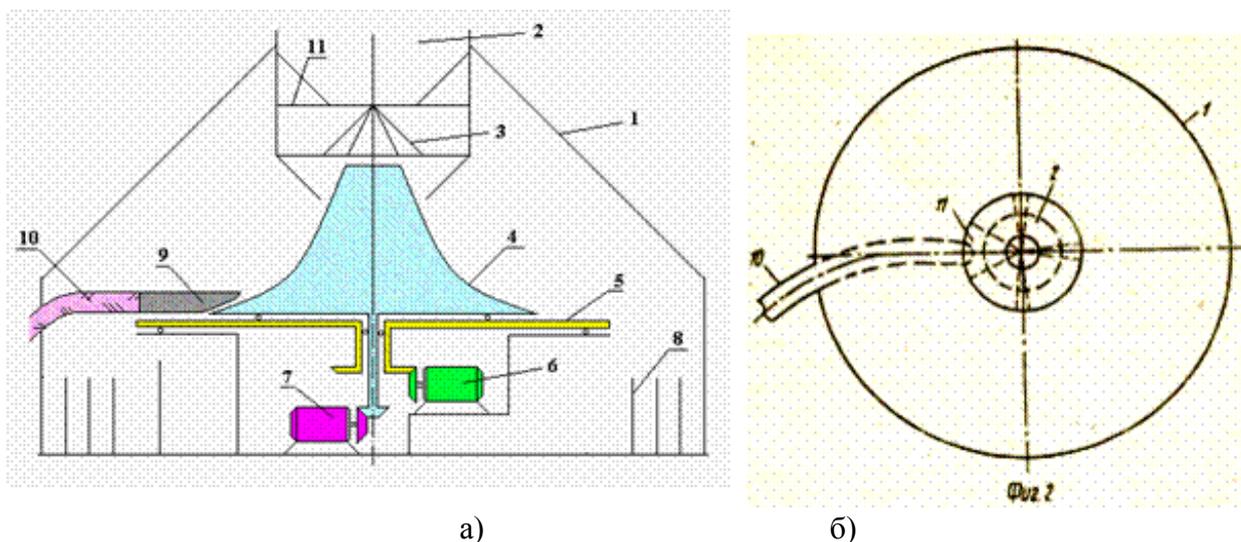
Фрикционный сепаратор: осевой разрез (а) и вид сверху (б): 1 – корпус, 2 – бункер, 3 – питатель, 4 – приспособления для равномерной подачи питания, 5 – фрикционная поверхность, 6,7 – привод фрикционной поверхности и равномерной подачи питания, 8 – емкости для продуктов разделения, 9 – очиститель, 10 – пылеотводящий патрубок, 11 – защитный кожух
